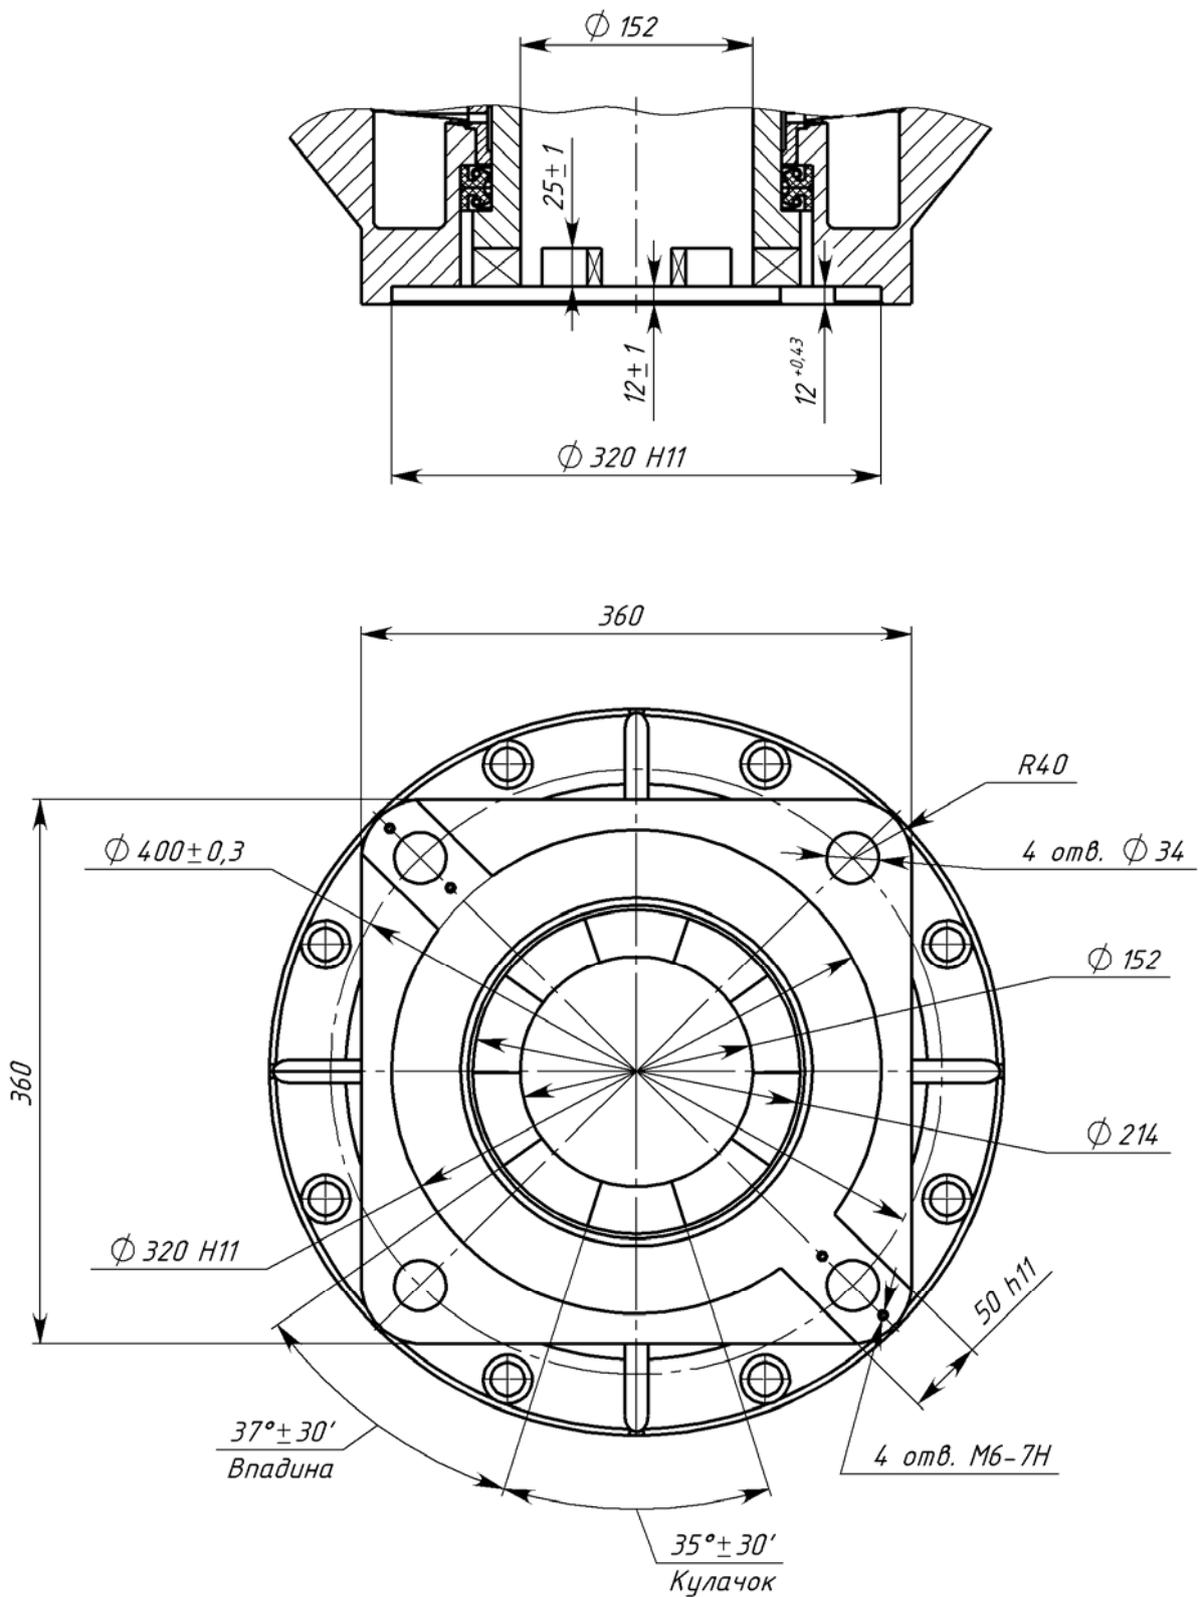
Присоединение типа Д для конструктивной схемы 44
